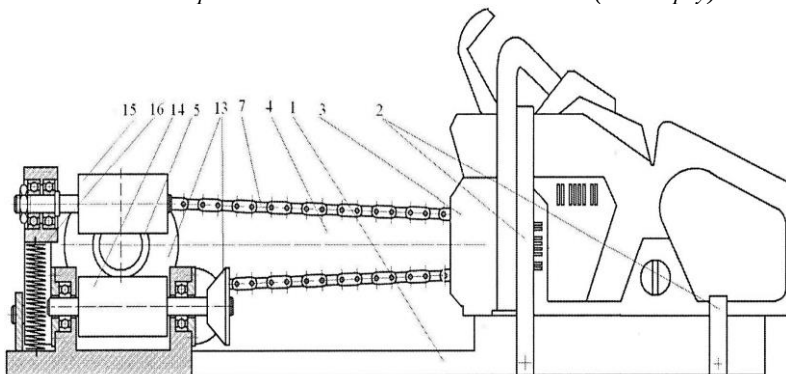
Устройство для заготовки хвойной лапки (вид сзади)
